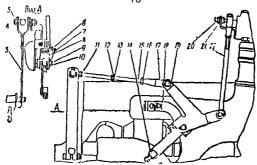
Установка деталей акселератора автомобиля ГАЗ-52-07
